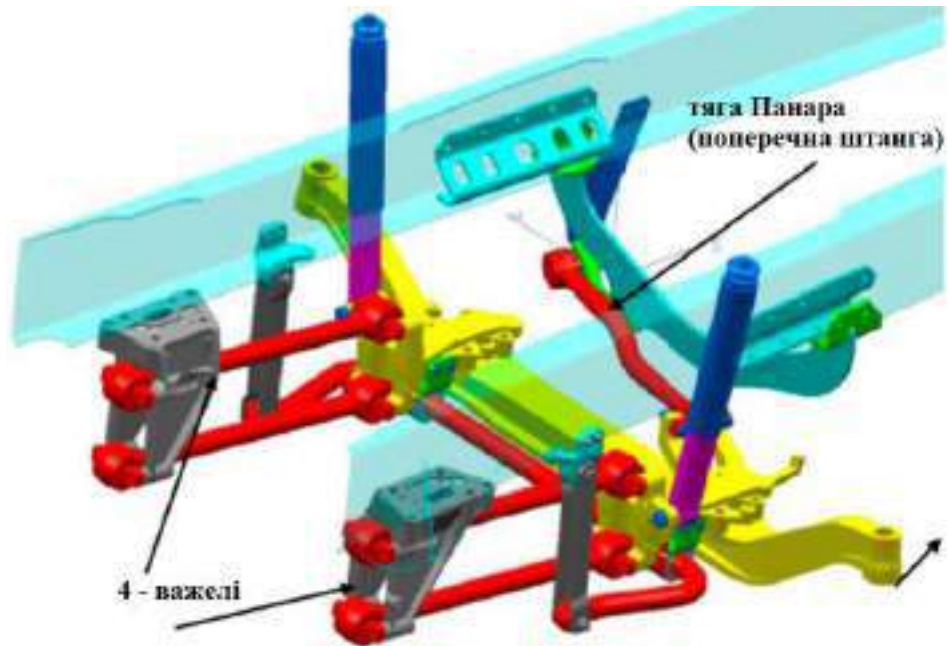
Стара конструкція передньої пневматичної підвіски.
